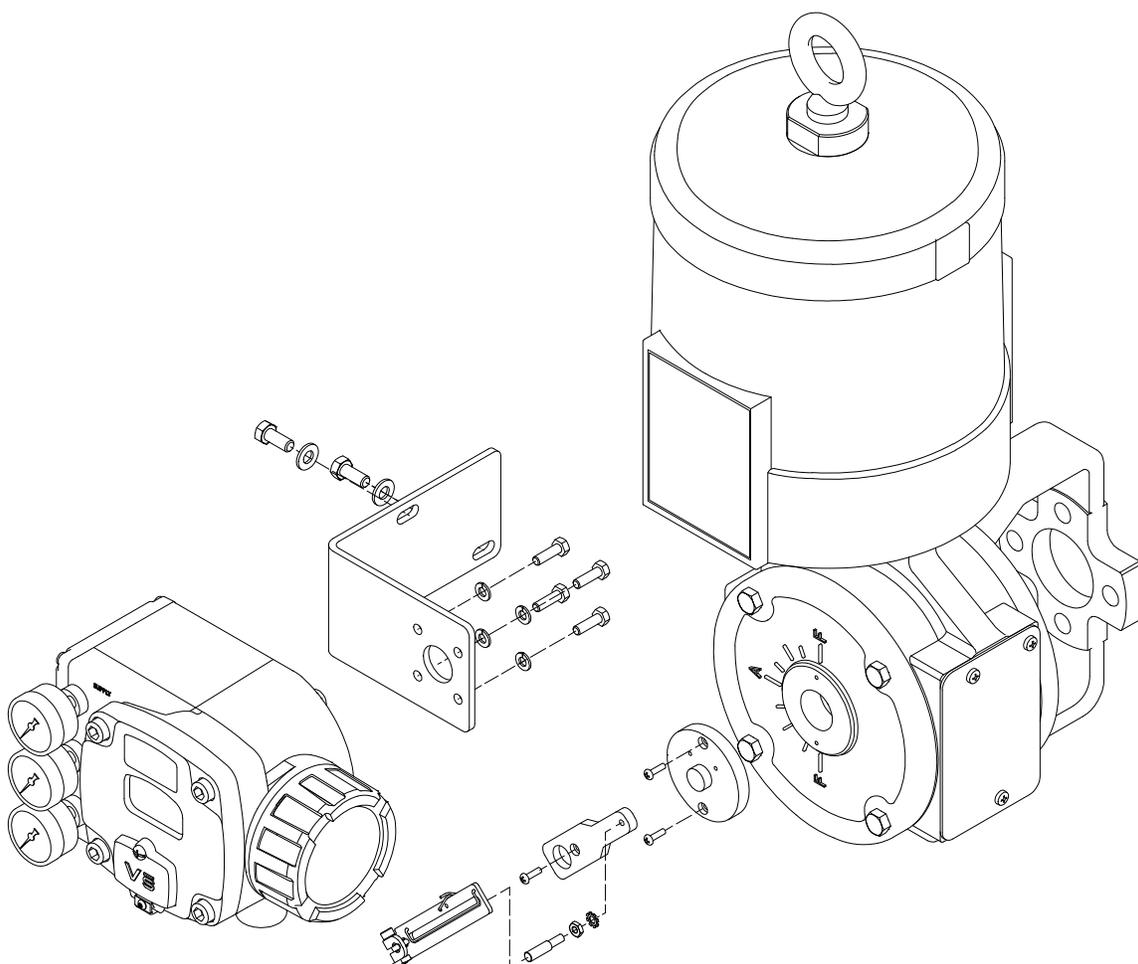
Montagem do posicionador Chronos no atuador rotativo da válvula ĒL (configuração ar-para-abrir / falha-fecha)
